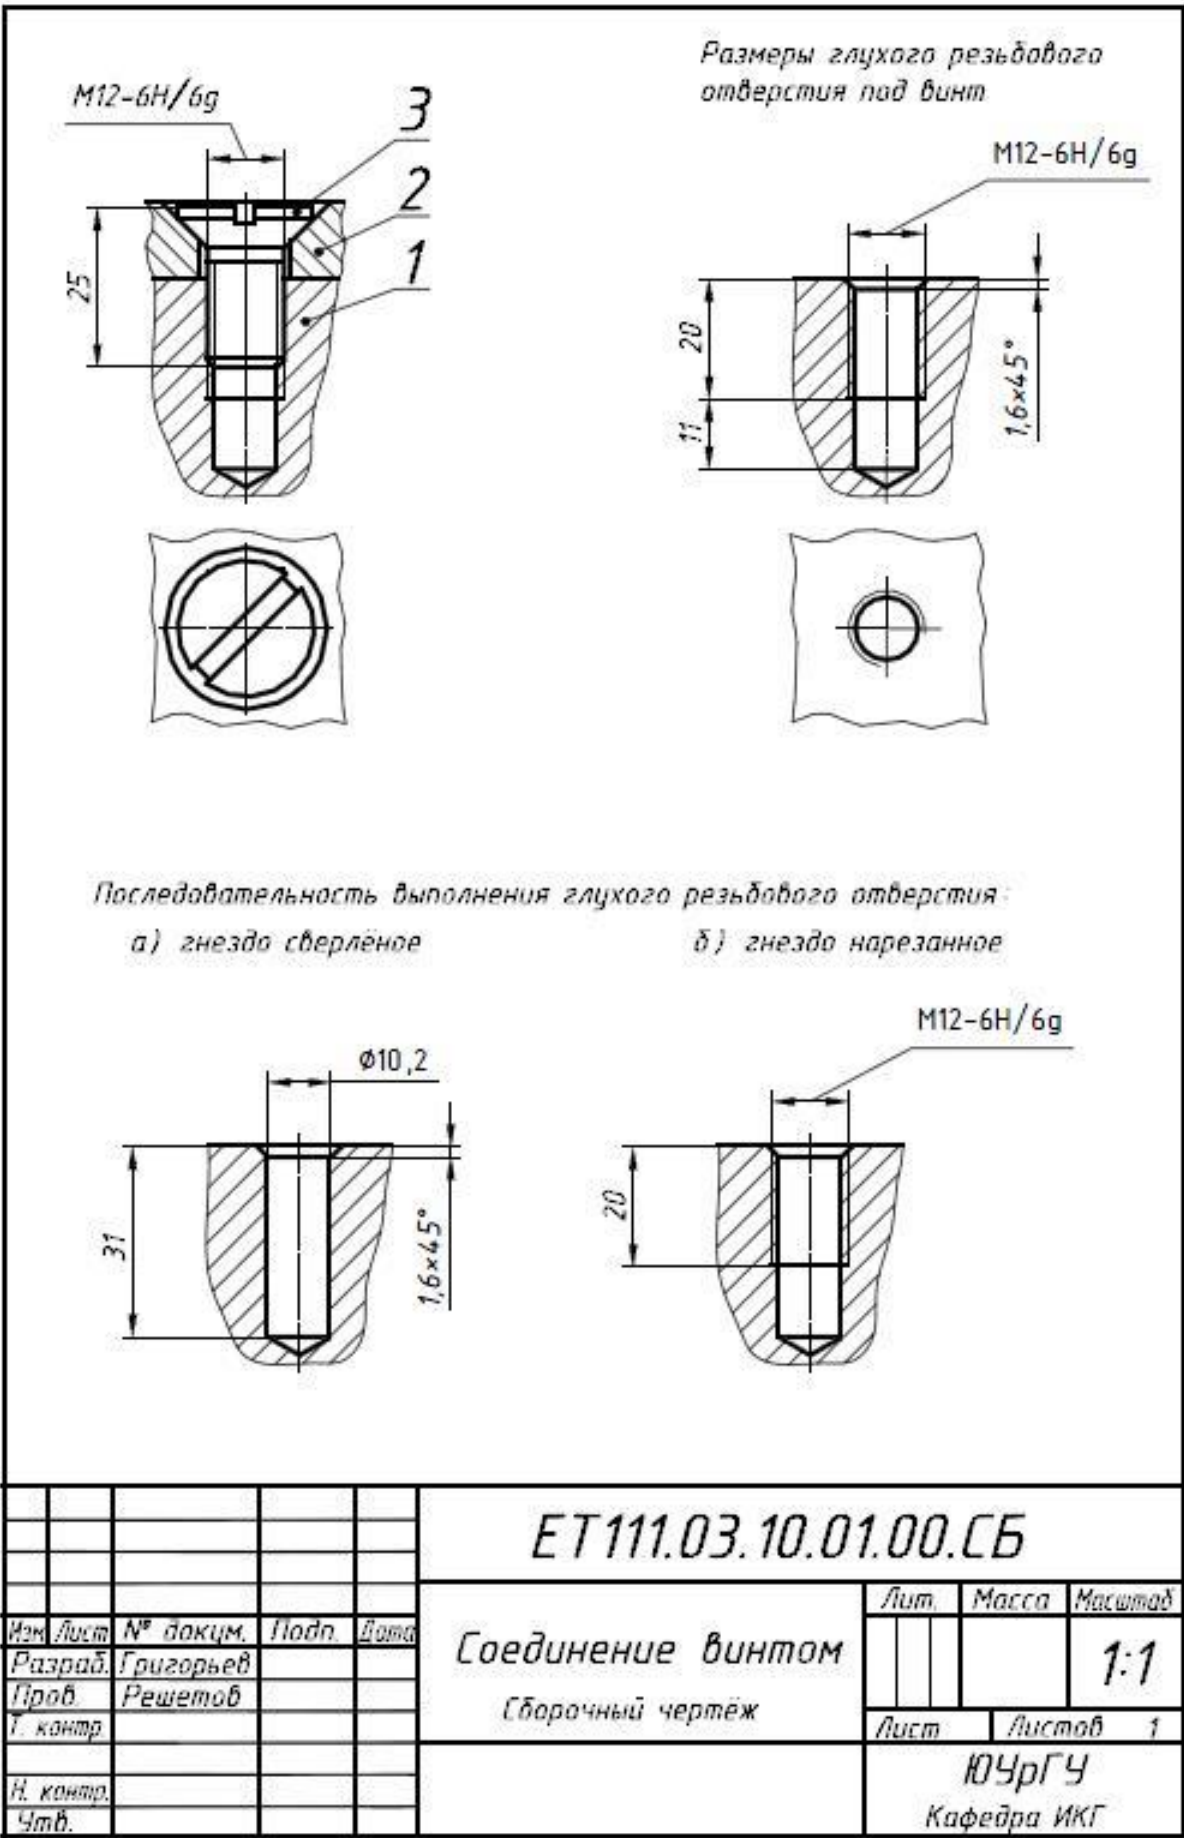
Пример выполнения сборочного чертежа «Соединение винтом»
